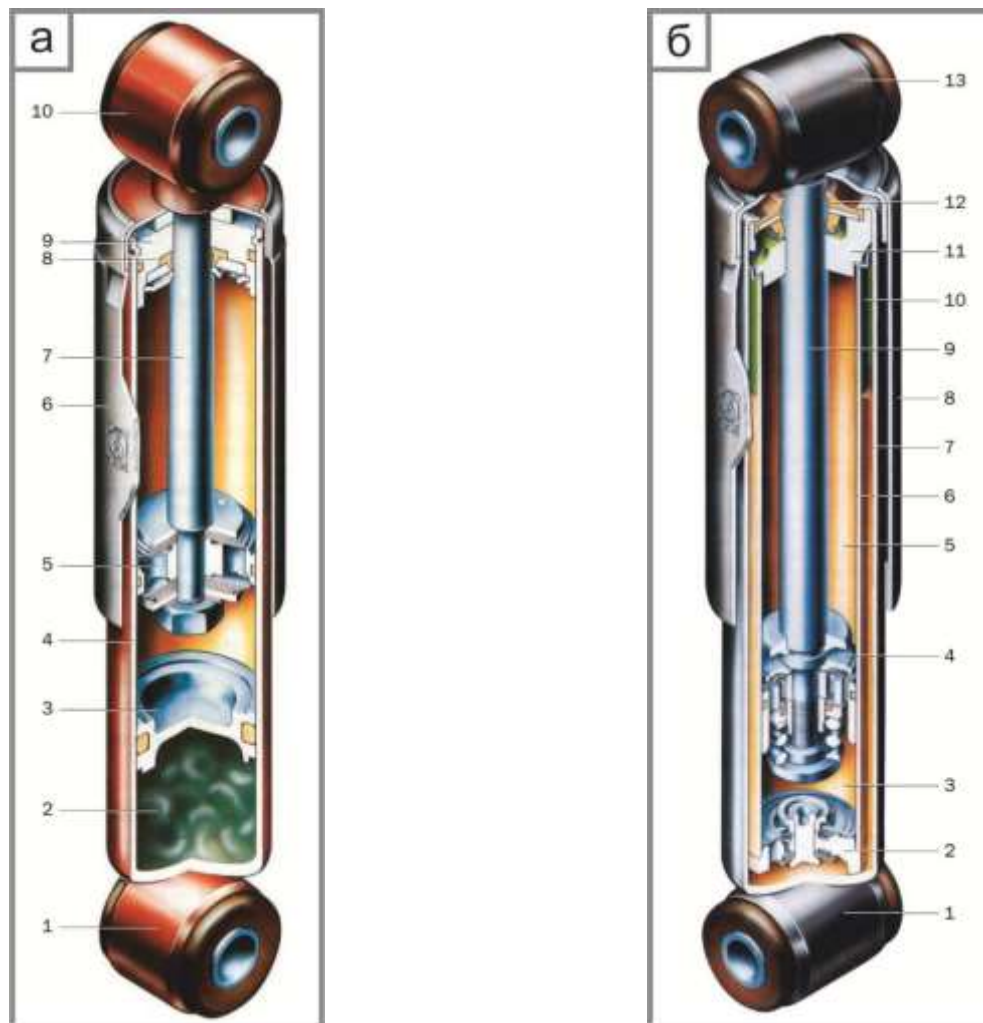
Конструкція (а) телескопічного однострубіного амортизатора: 1 – нижня провушина; 2 – газ; 3 – плаваючий поршень; 4 – робочий циліндр; 5 – поршень; 6 – корпус; 7 – шток поршня; 8 – сальник штока; 9 – напрямна штока; 10 – верхня провушина; і (б) телескопічного двотрубіного амортизатора: 1 – нижня провушина; 2 – донний клапан; 3, 5 – робоча порожнина; 4 – поршень; 6 – робочий циліндр; 7 – корпус резервуара; 8 – корпус; 9 – шток поршня; 10 – повітря; 11 – напрямна штока; 12 – сальник штока; 13 – верхня провушина
